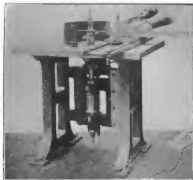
u. 68. Die Wiener Fräsmaschine.
